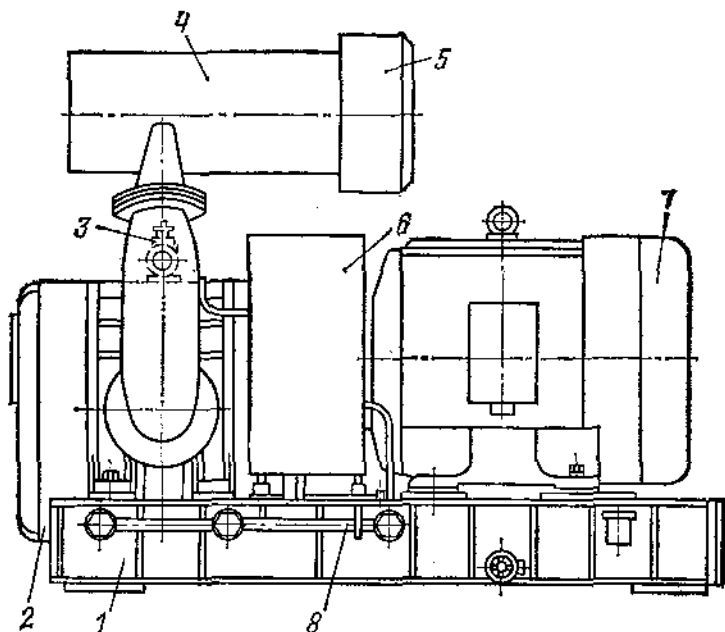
Компрессорная установка 2ВД-12/2,5:
